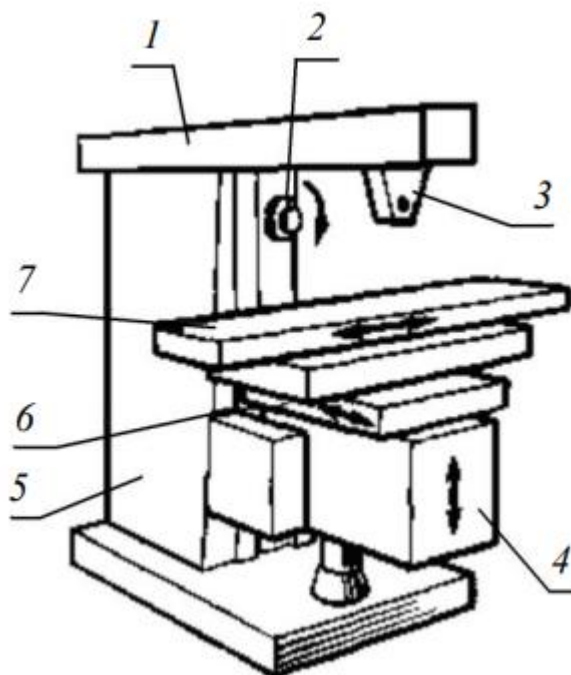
Схема фрезерного консольно-горизонтального верстата:
